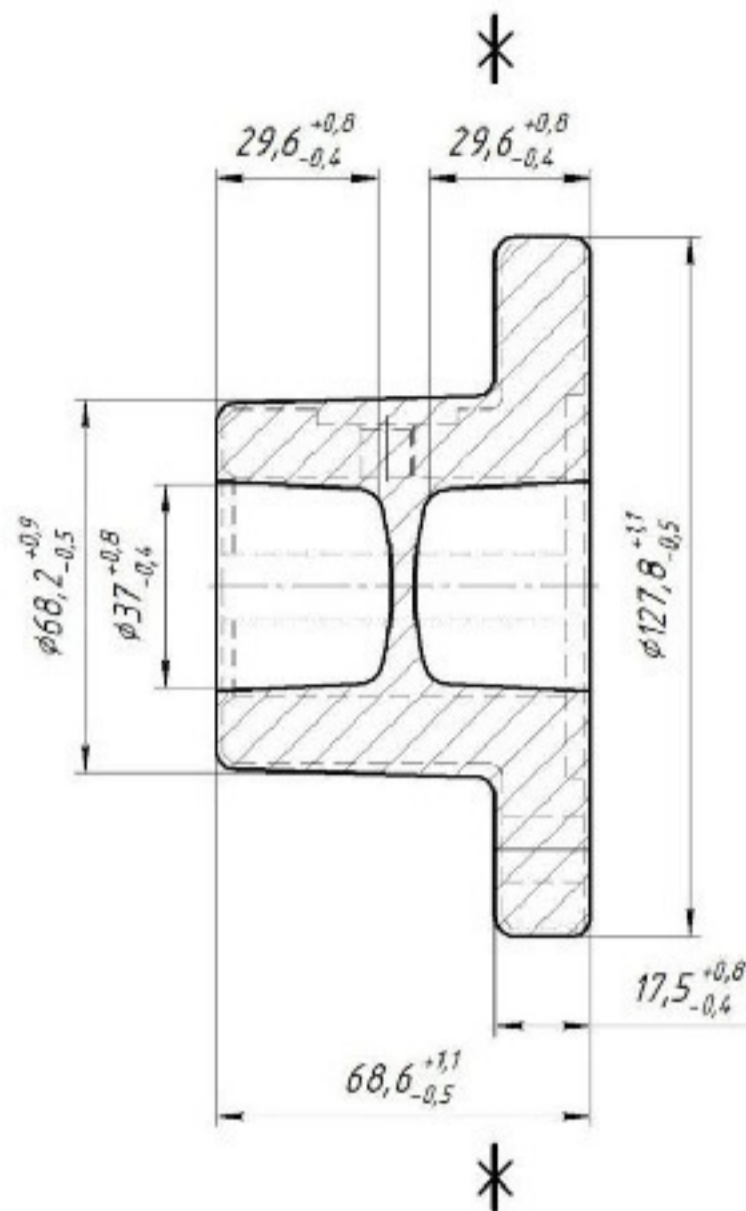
Ескіз заготовки при штампуванні на ГША
